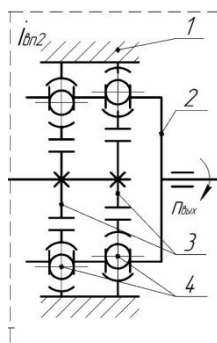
Кинематическая схема волновой двухступенчатой передачи с промежуточными телами качения:
